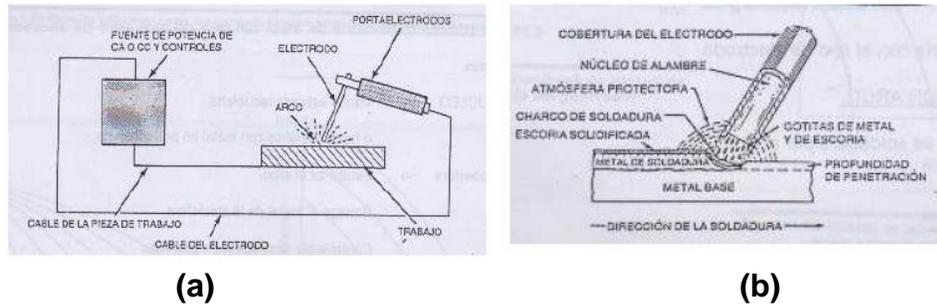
Soldadura manual eléctrica por arco con electrodo revestido- SMAW. (a).- Elementos del circuito. (b).- Estructura de la soldadura.¹⁶
